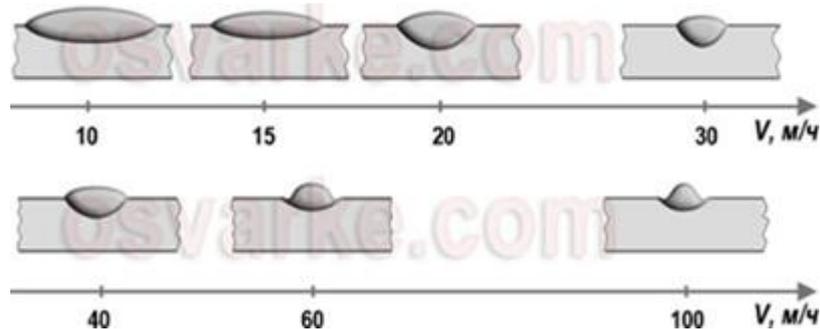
Влияние скорости сварки на форму и размеры шва
